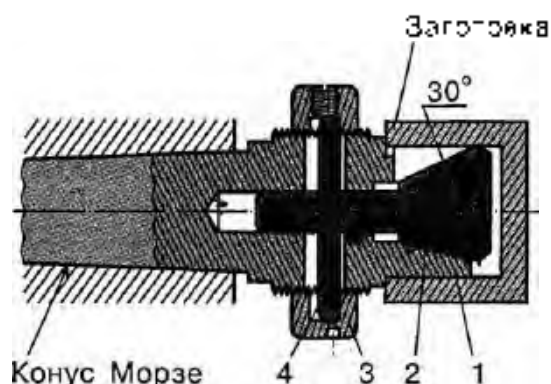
ЦАНГОВА ОПРАВКА ДЛЯ ОБРОБКИ СТАКАНІВ.
